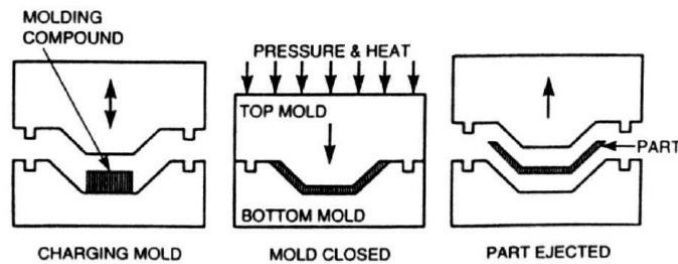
Esquema del equipo de conformado por molde a compresión. [7]
